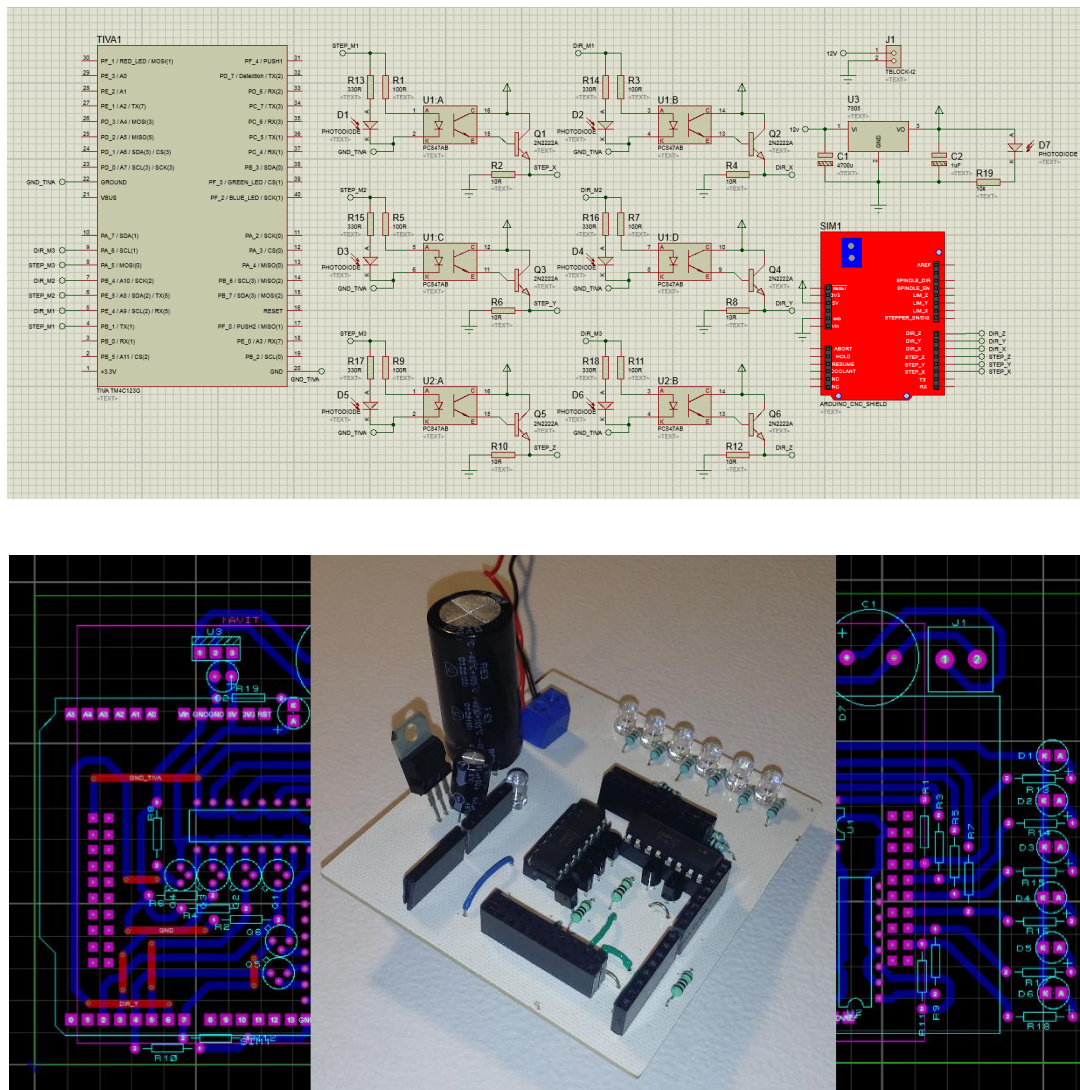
Esquemático y diseño PCB de placa de opto acoplamiento
